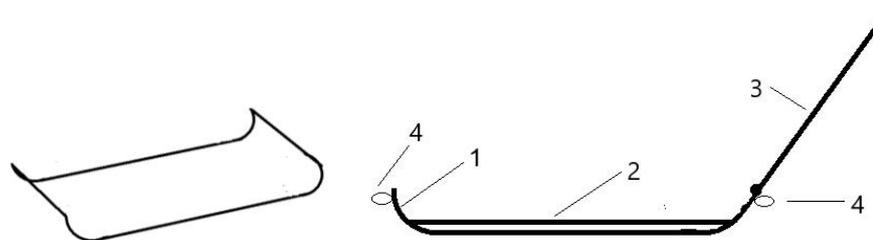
модель и конструкция санки на полозьях: 1 - полозья трубчатые металлические, 2 - поддон, 3 - толкатель, 4 - крючки для крепления веревки
